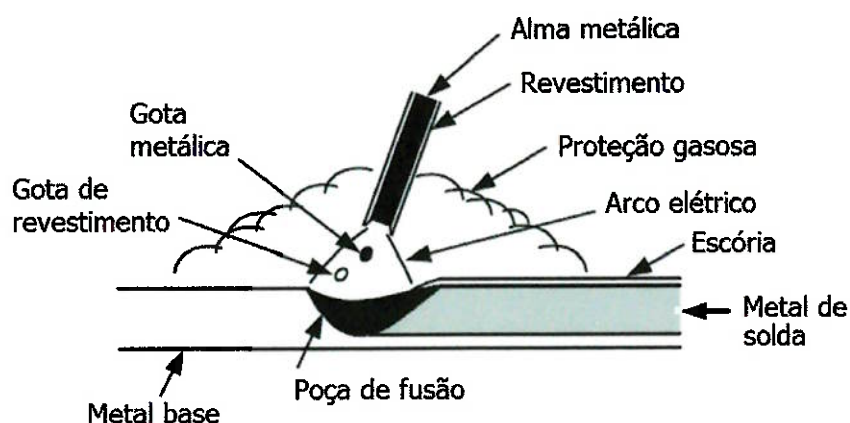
Processo de soldagem ao arco com eletrodos revestidos [7, adaptado]
